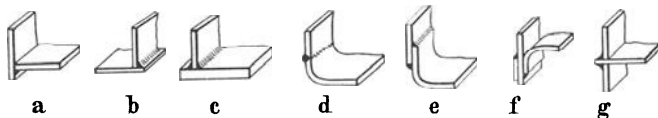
Geschweißte Kasten- und Behälterecken.
